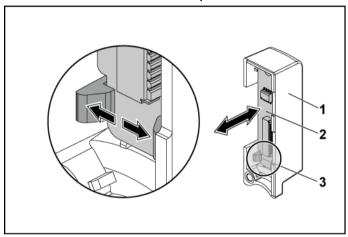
Retrait et installation d'un ensemble panneau avant
